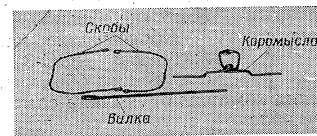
Общий вид деталей, необходимых для подготовки пакета к сбрасыванию с самолета
